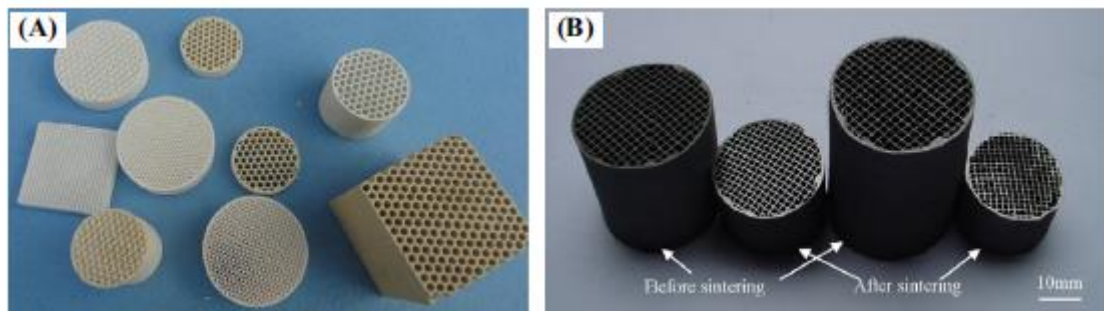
Topología de ciertas estructuras fabricadas mediante sinterizado [1].
